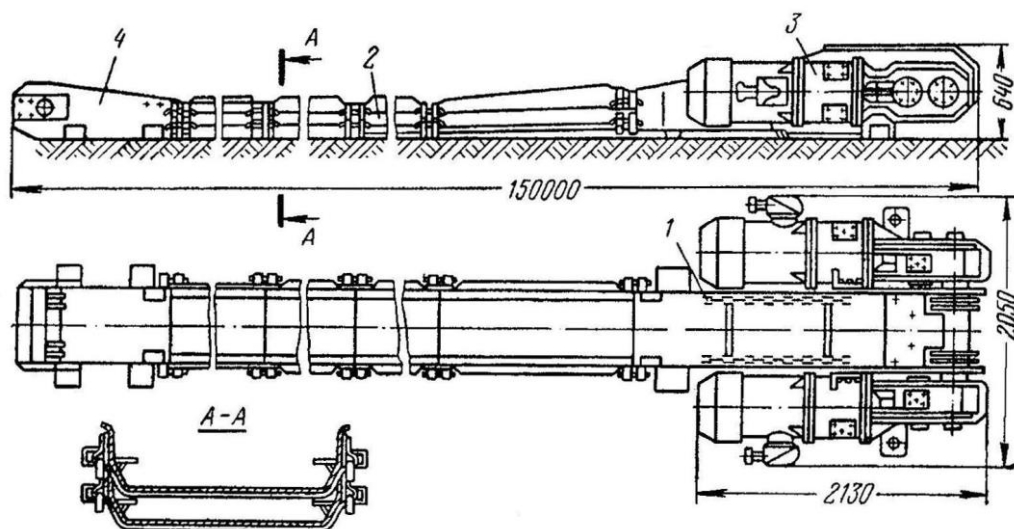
Типовий скребковий розбірний конвеєр:
